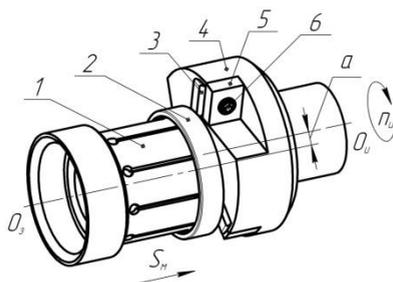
Подрезка торцов колец шарикоподшипников способом лобового точения
